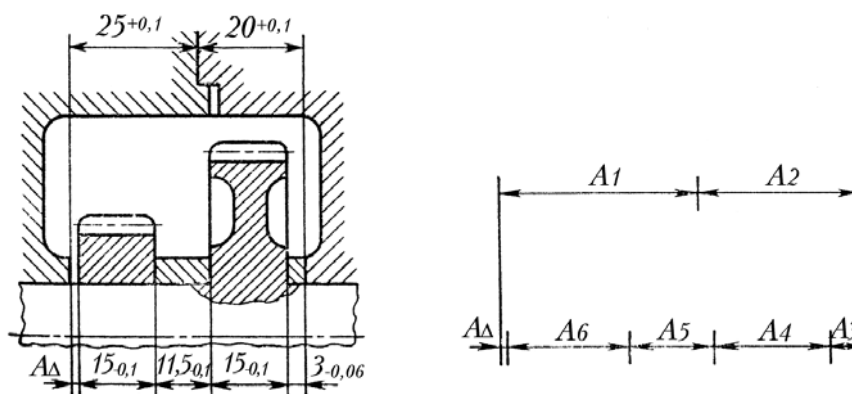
Внешний вид редуктора и размерная цепь.
